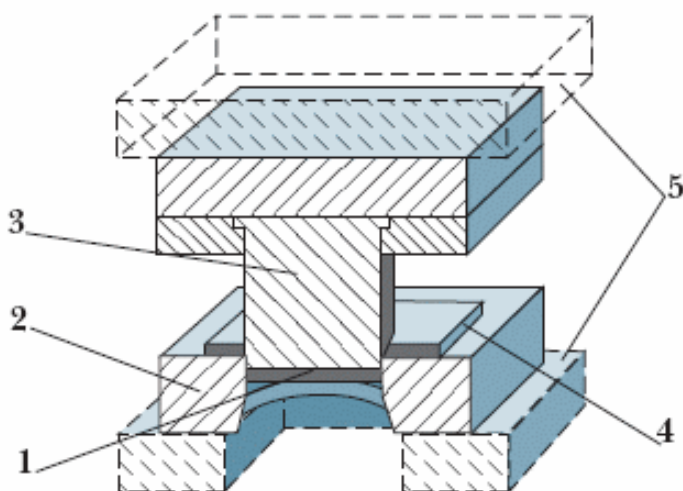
Схема расположения заготовки в вырубном штампе при листовой штамповке:
